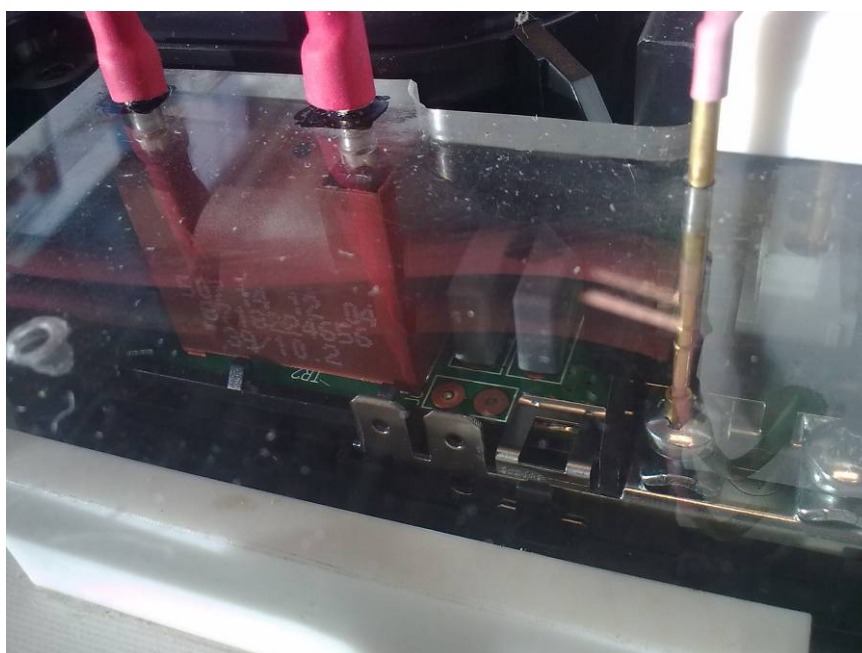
Agulhas do jig (fechado) em contacto com o pcb – alta tensão.
